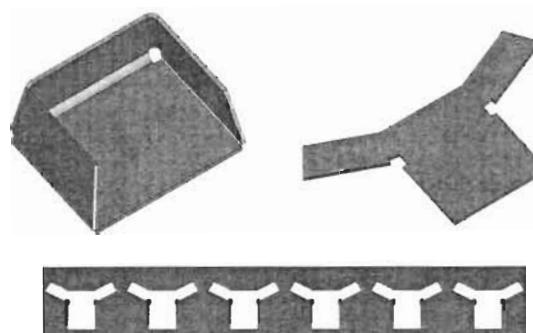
Modelo de Chapa Metálica en 3D y aplanoado.
